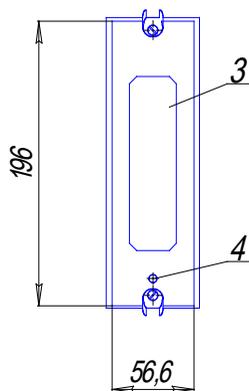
Габаритные и установочные размеры прибора Ф34.2
